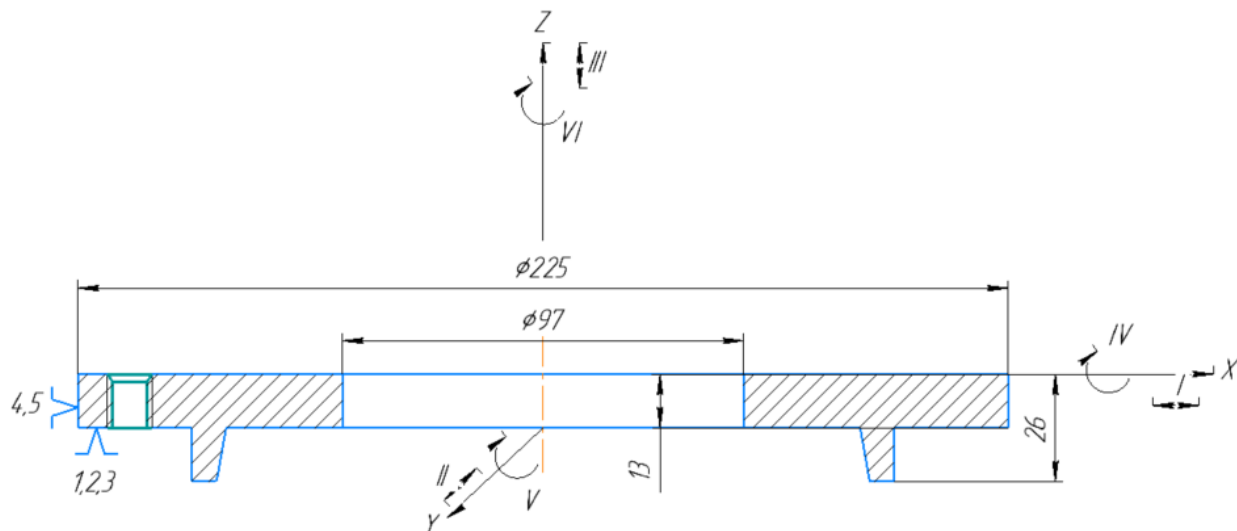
Схема установки заготовки в 3-х кулачковый патрон за торець 225 і зовнішню поверхню 225
